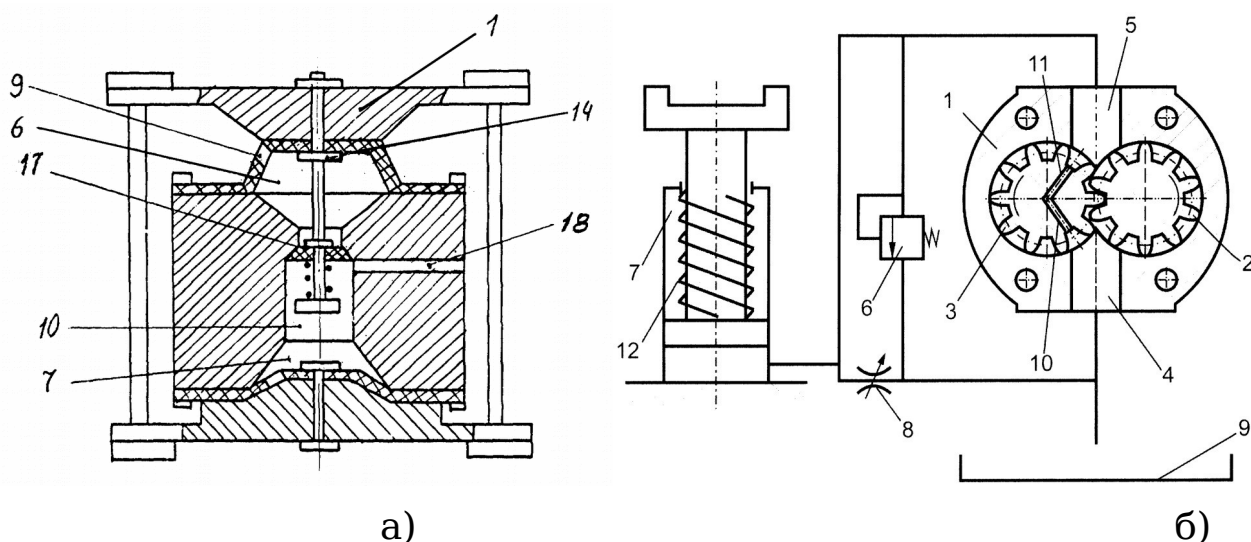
а) Кинематический вибровозбудитель б)
